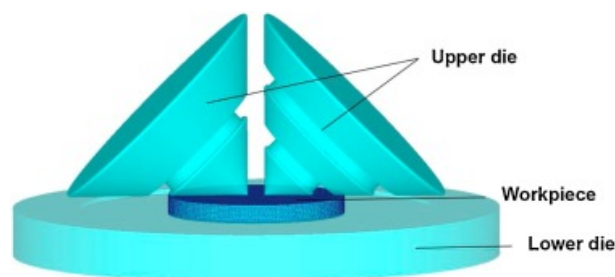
Схема ротационнойковки несколькими вращающимися инструментами
